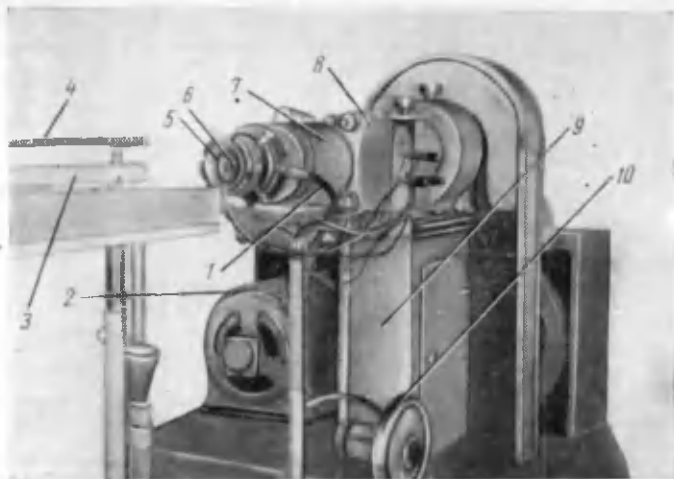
Внешний вид шприц-пресса для изготовления полихлорвиниловой трубки:
